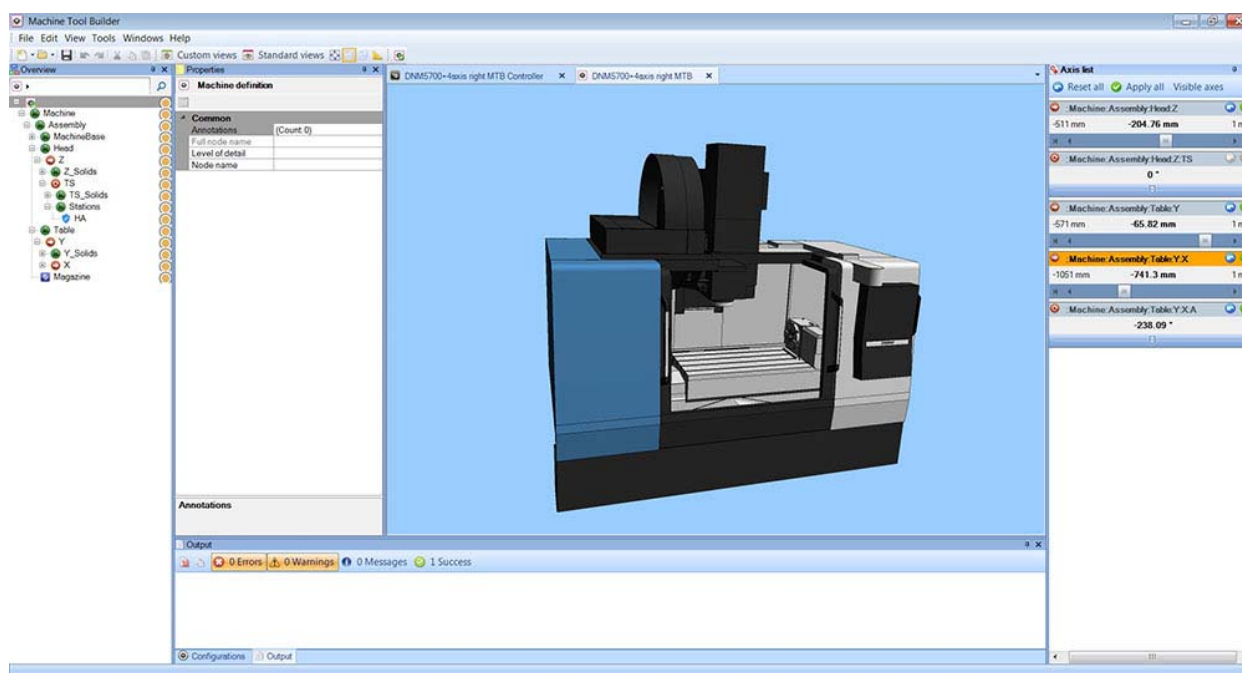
Приложение Machine Tool Builder для построения станочной среды
